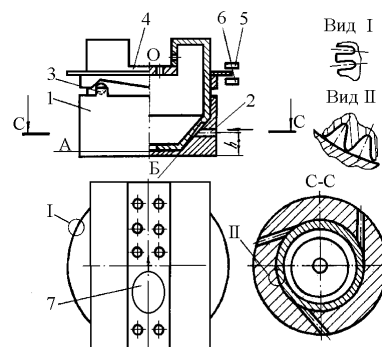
Устройство для бесконтактных взвешивания и сортировки штучных изделий по массе: 1 - корпус; 2 - дроссели для подачи сжатого воздуха; 3 - шаровая опора; 4 - промежуточная платформа-ротор; 5 - световой излучатель; 6 - фотоэлемент; 7 - изделие.
